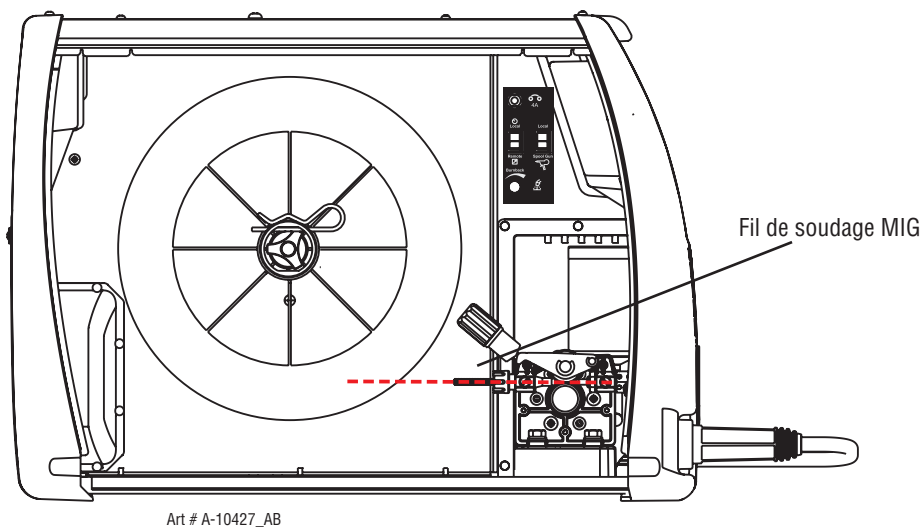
Fil de soudage MIG - Installation
